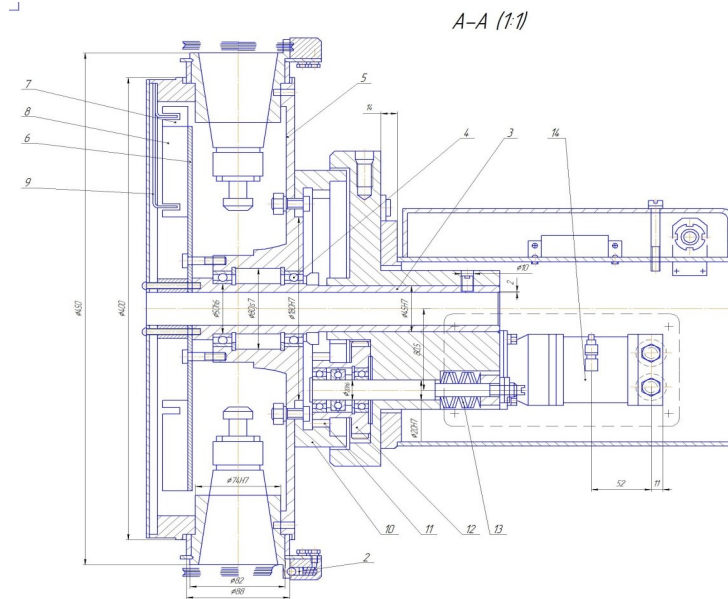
Інструментальний магазин - поздовжній розріз
